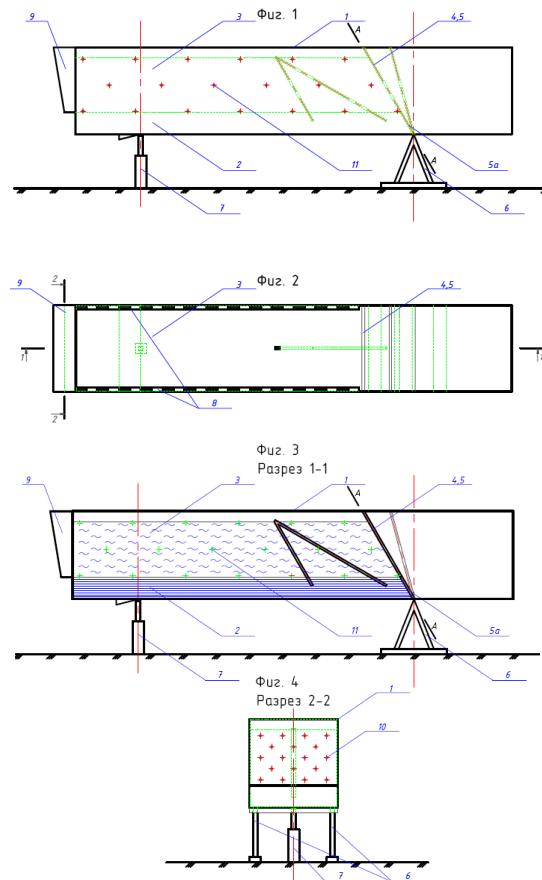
Конструкция стендов для проведения испытаний. Фиг.1 – вид сбоку, фиг.2 – вид сверху, фиг. 3 – разрез продольный, фиг. 4 – разрез поперечный
